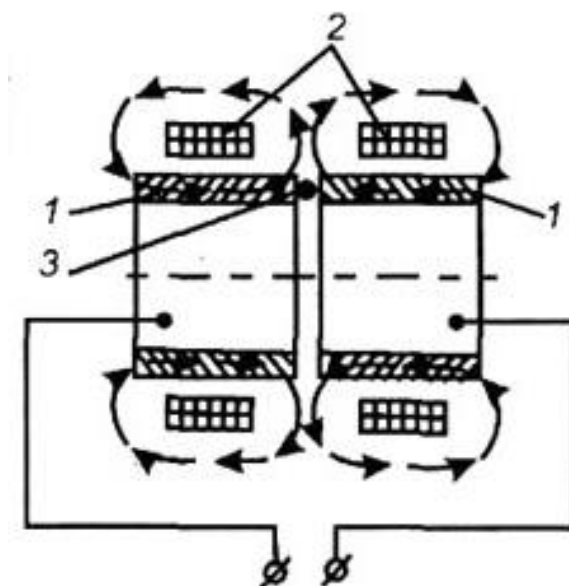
Сварка дугой, вращающейся в магнитном поле:
